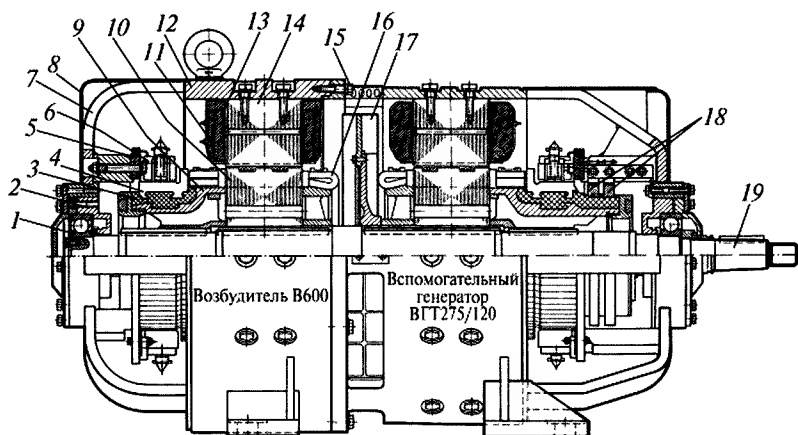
Двухмашинный агрегат типа А706Б:
